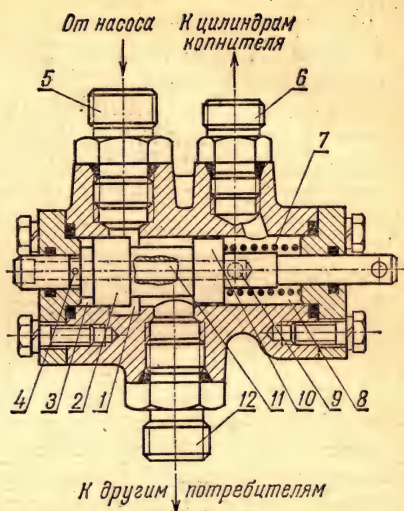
Распределитель гидроавтоматической системы копнителя 44-8Б (для комбайнов СК-4А и СКД-5) или 54-8Б (для комбайна СК-5):
